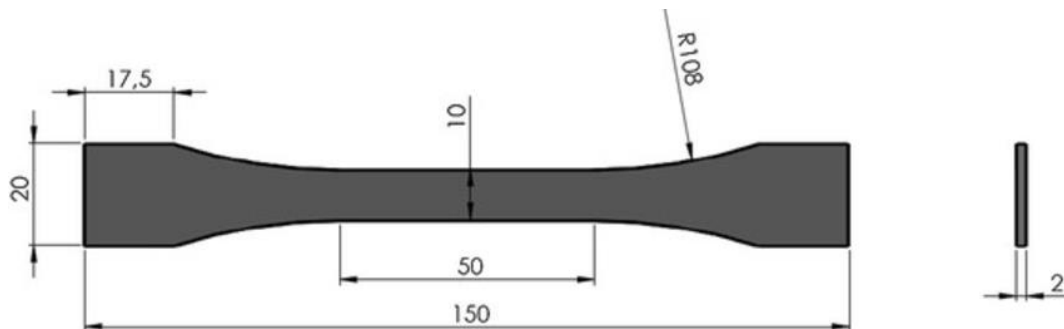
Dimensões dos provetes maciços de adesivo de acordo com a norma NF T 76-142 (dimensões em mm).
